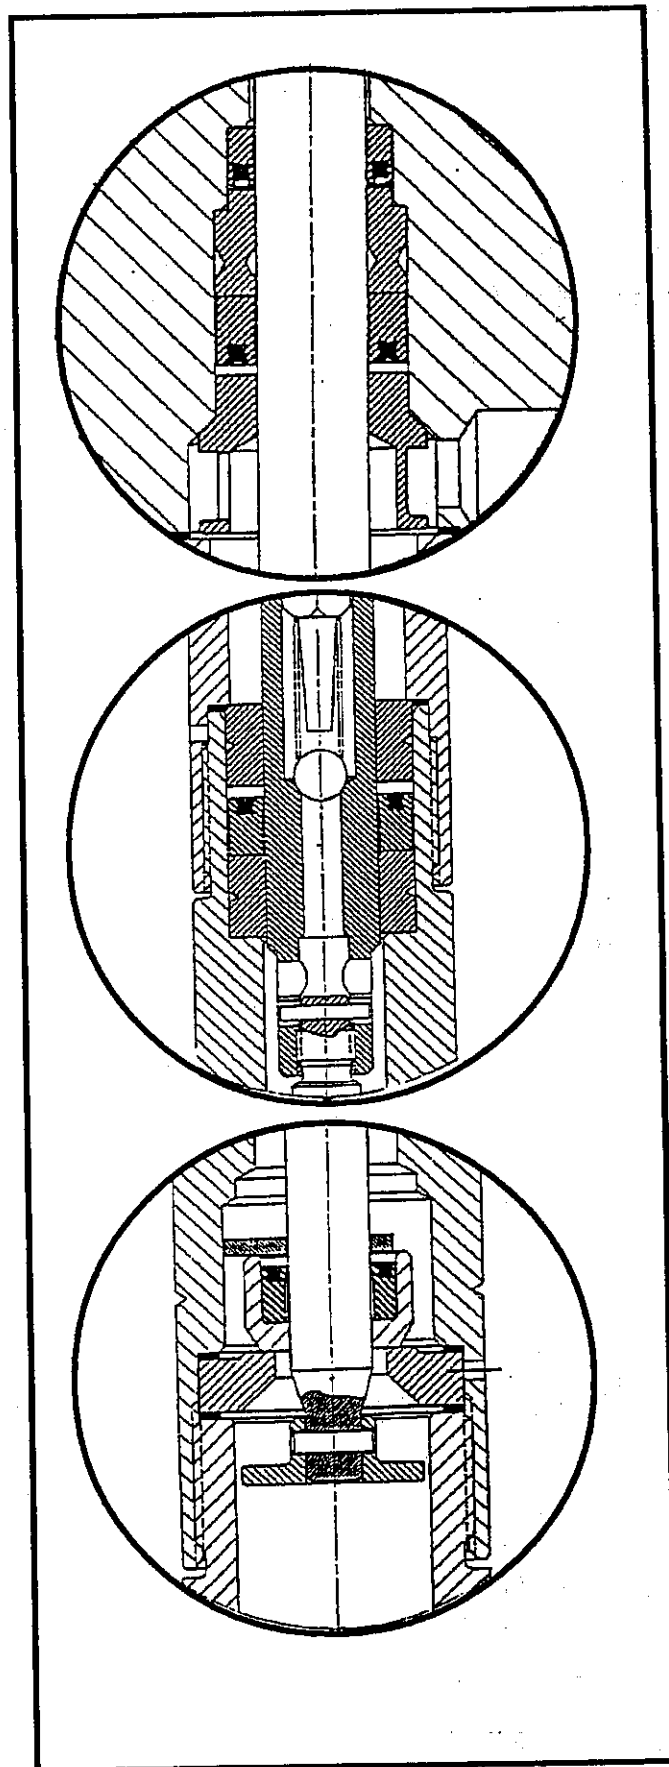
Vue en coupe des zones de joints d'étanchéité du tube de pompe
